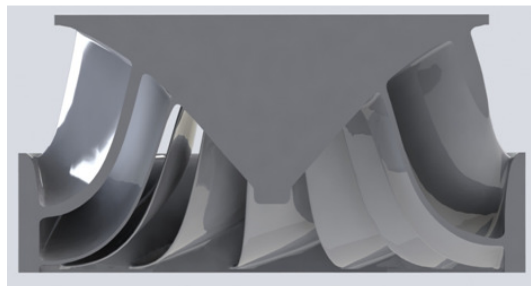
Modelagem 3D obtida do rotor escaneado – Vista e corte
